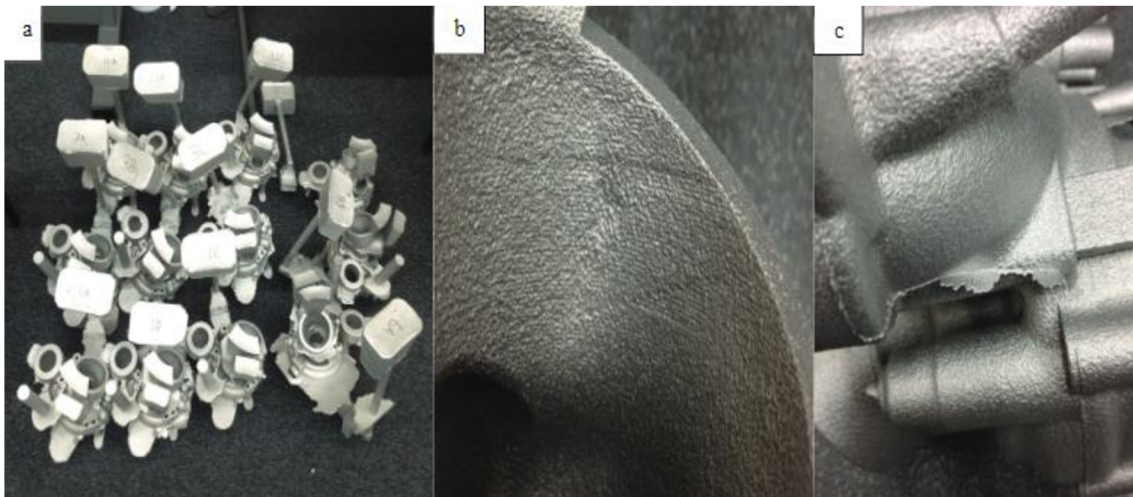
Komponenty vyrobené pomocí Laser Sintering Metal [8]
